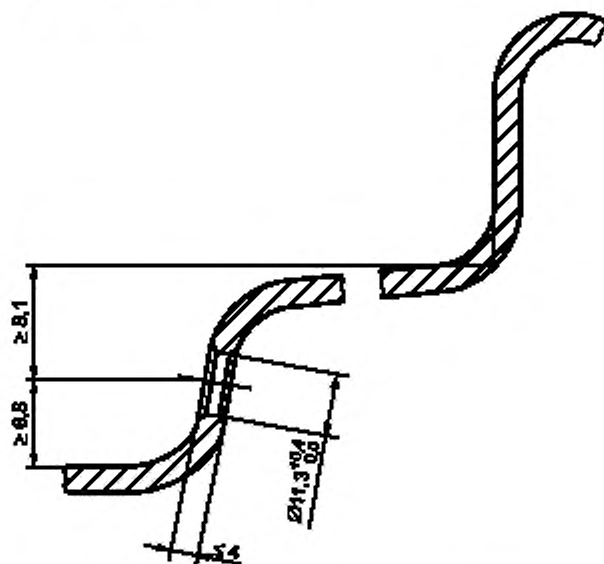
Размеры вентиляного отверстия для бескамерных шин
